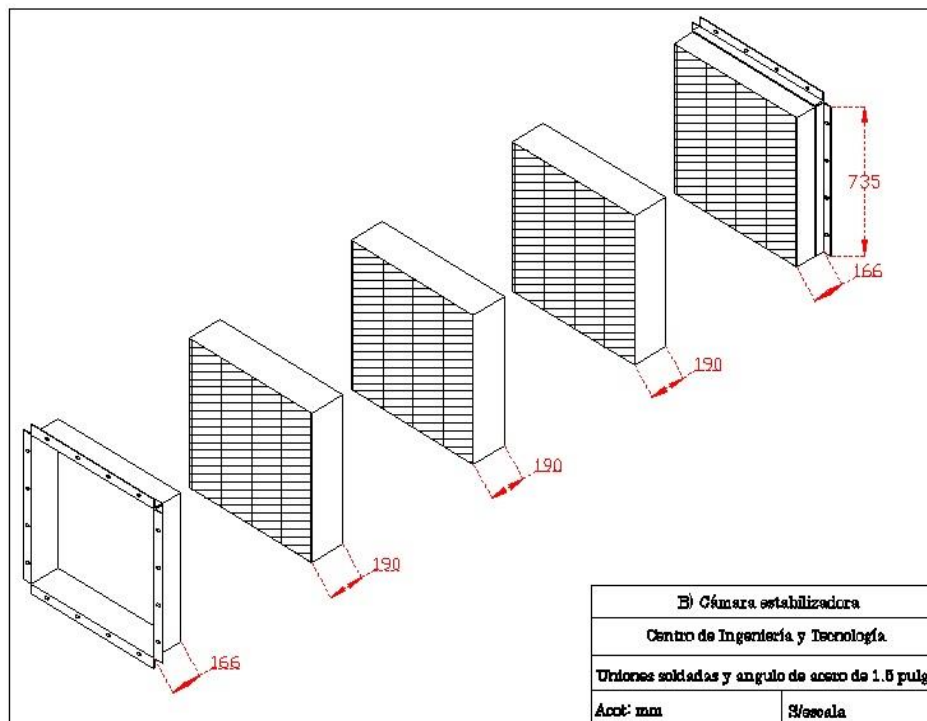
Vista isométrica de las uniones soldadas en la cámara estabilizadora.
